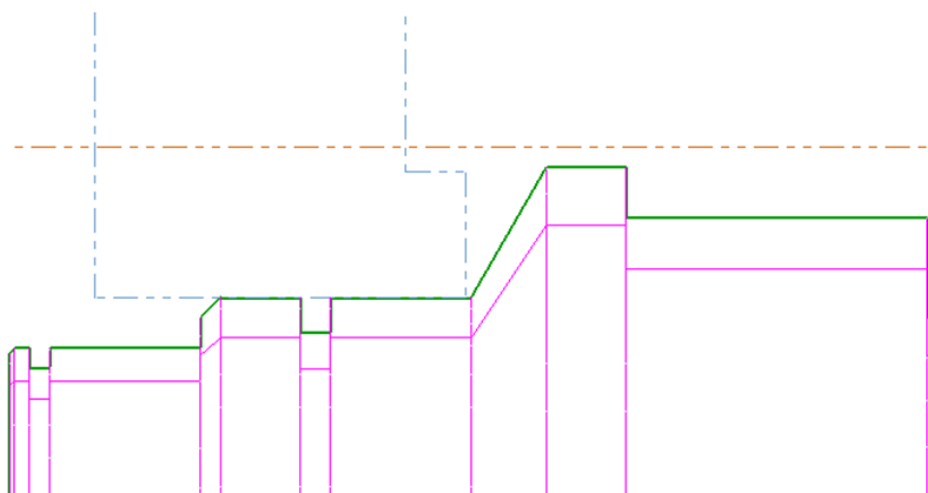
Nastavení hladiny při otočení obrobku pomocí příkazu Dráhy nástrojů/Různé/Otočit obrobek
